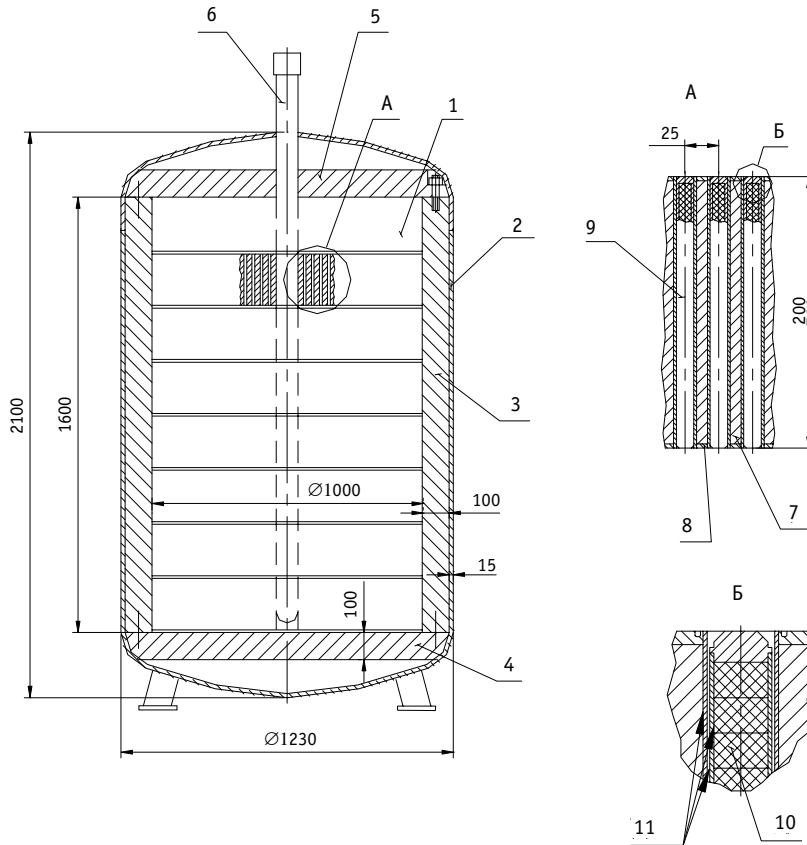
Эскиз реактора МАСТЕР-ИАТЭ: 1 - активная зона; 2 - корпус; 3 - отражатель боковой; 4 - отражатель нижний; 5 - отражатель верхний; 6 - канал системы регулирования; 7 - замедлитель; 8 - очехловка замедлителя; 9 - твэл; 10 - топливный сердечник; 11 - контактный подслои
